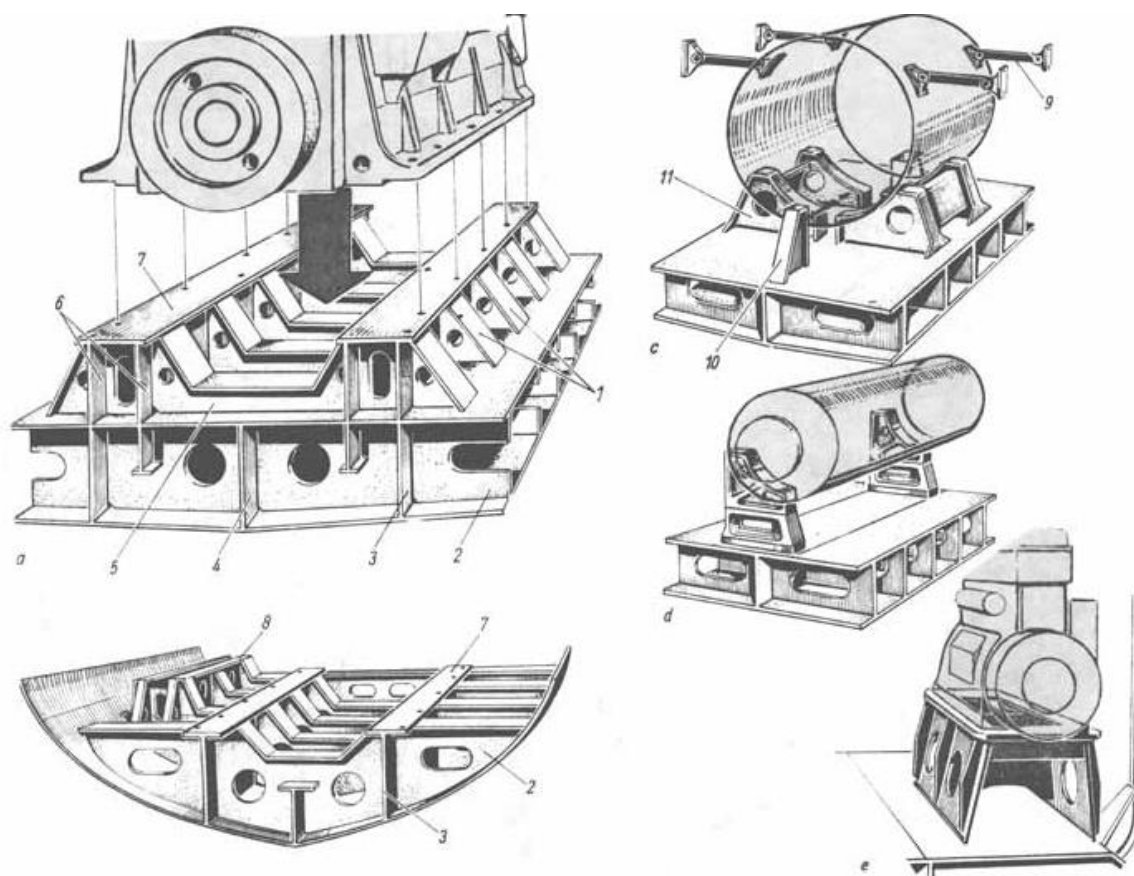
Типы судовых фундаментов и их размещение: 1 – кницы с поясками; 2 – флор; 3 – стрингер днищевой; 4 – вертикальный киль; 5 – brackets поперечные; 6 – продольные балки; 7 – опорные горизонтальные полосы; 8 – фундамент вспомогательного двигателя; 9 – анкерная связь; 10 – стопор котла; 11 – седельная опора; а – фундамент главного двигателя на настиле второго дна; б – фундамент главного двигателя на одинарном дне; с – фундамент для цилиндрического огнетрубного котла; д – фундамент для водотрубного котла; е – фундамент для компрессора
